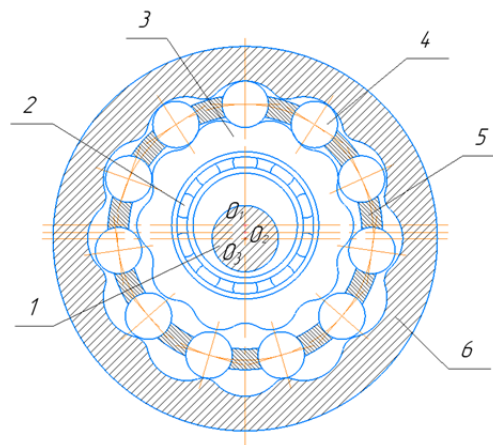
Схема передачи с ПТК с двумя циклоидальными колесами
